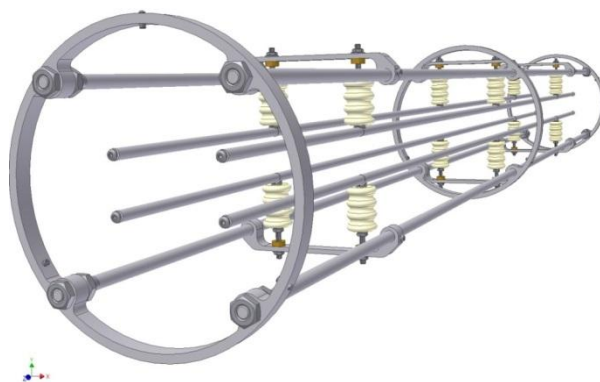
Вид ударного магнита с опорной конструкцией
